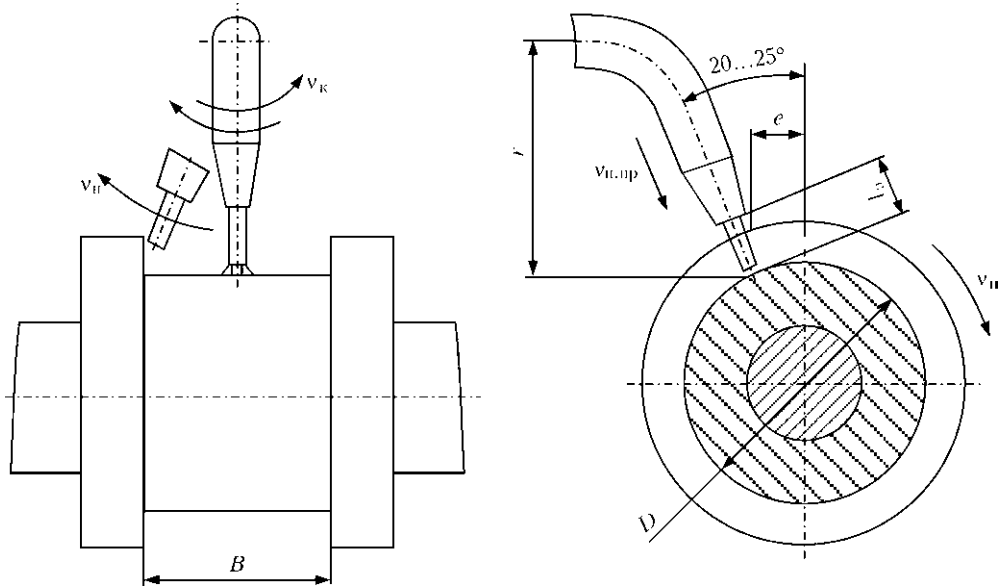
Схема техники широкослойной наплавки колеблющимся электродом (самозащитной порошковой проволокой) цилиндрических деталей (см. обозначения в тексте)
